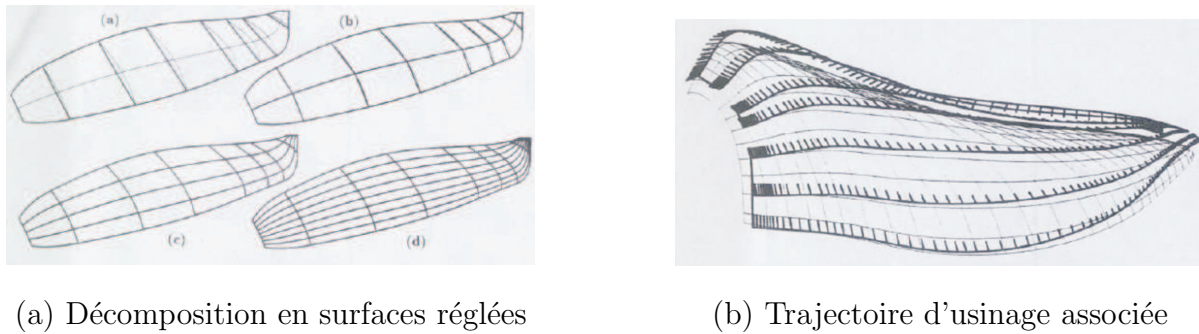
Usinage d'une surface quelconque par flanc d'outil
